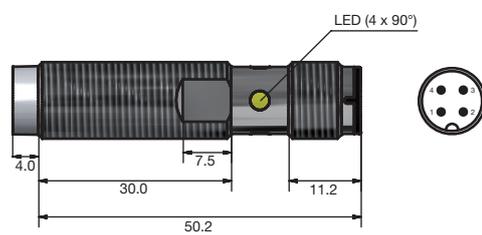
Kurze Ausführung, Nicht bündiger Einbau, Steckversion
